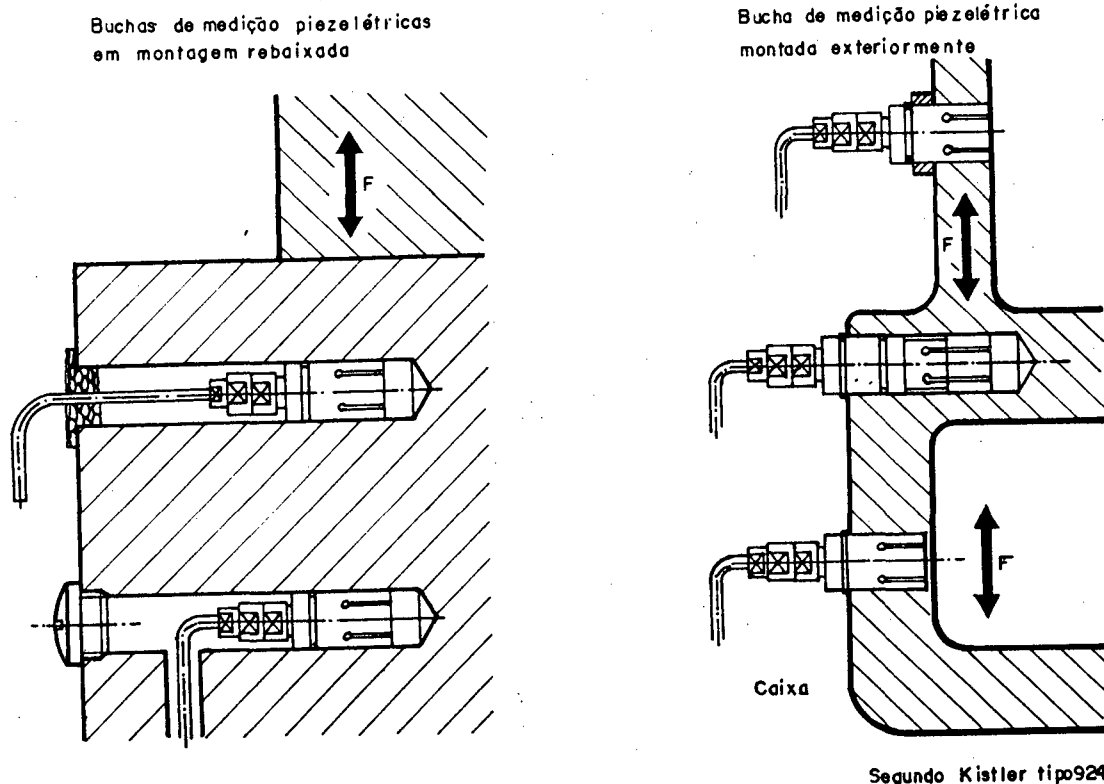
Variações de montagem de buchas de medição piezelétrica [9,72-73].
